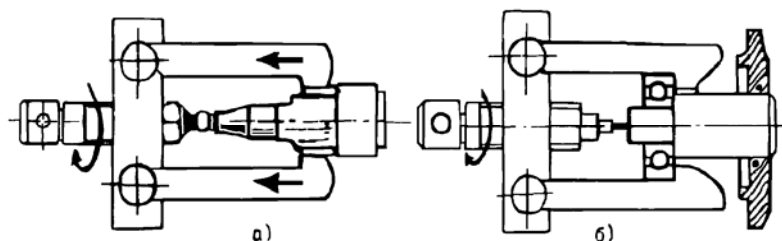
Приспособление для демонтажа подшипников качения:
